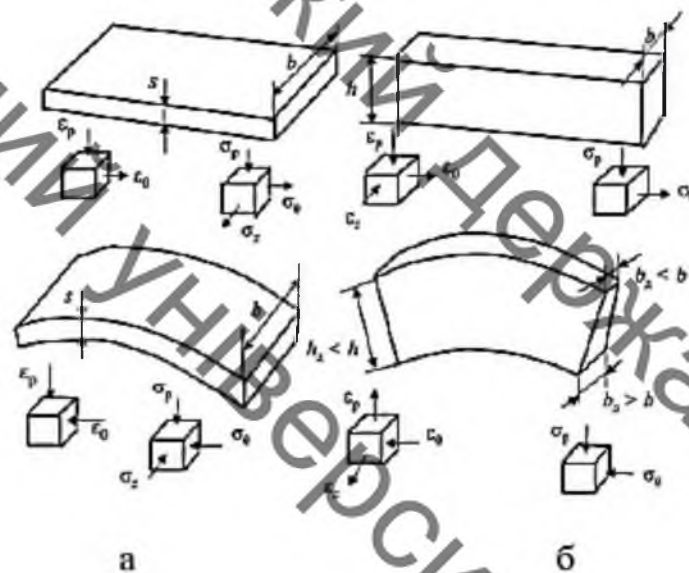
Схеми напруженого та деформованого станів при згинанні широких (а) та вузьких заготовок (б)
